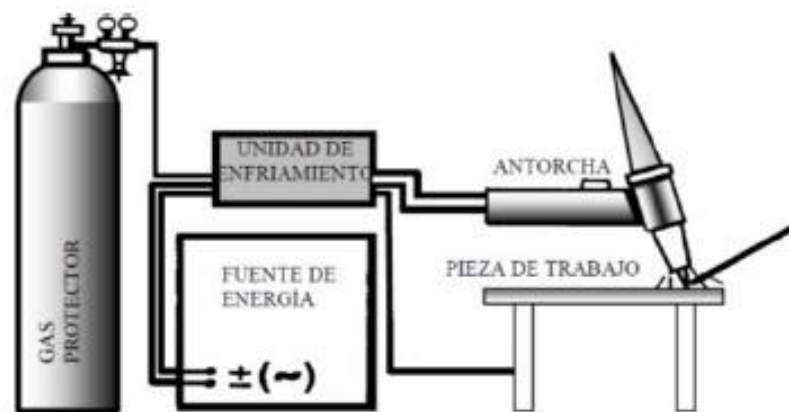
Estación de soldadura GTAW o TIG [28]
